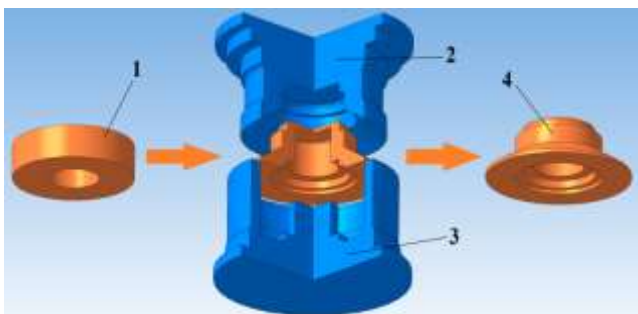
Схема объемной штамповки опорного изолятора из СВМПЭ-нанокompозита: 1 – заготовка; 2 - пуансон; 3- матрица; 4 – готовое изделие.
